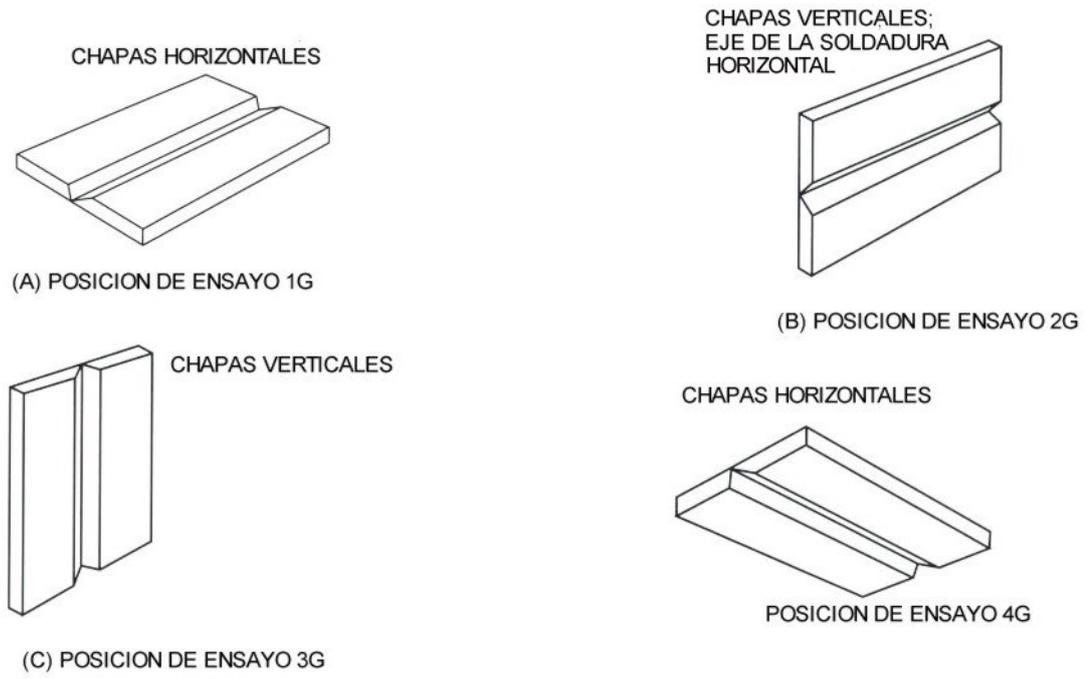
Posiciones de chapas de ensayo para soldaduras con bisel
